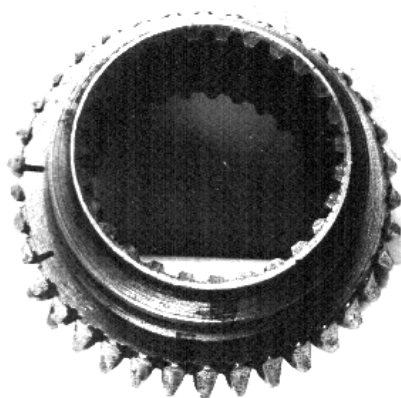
Разрушение шестерен коробки скоростей токарно-винторезного станка
